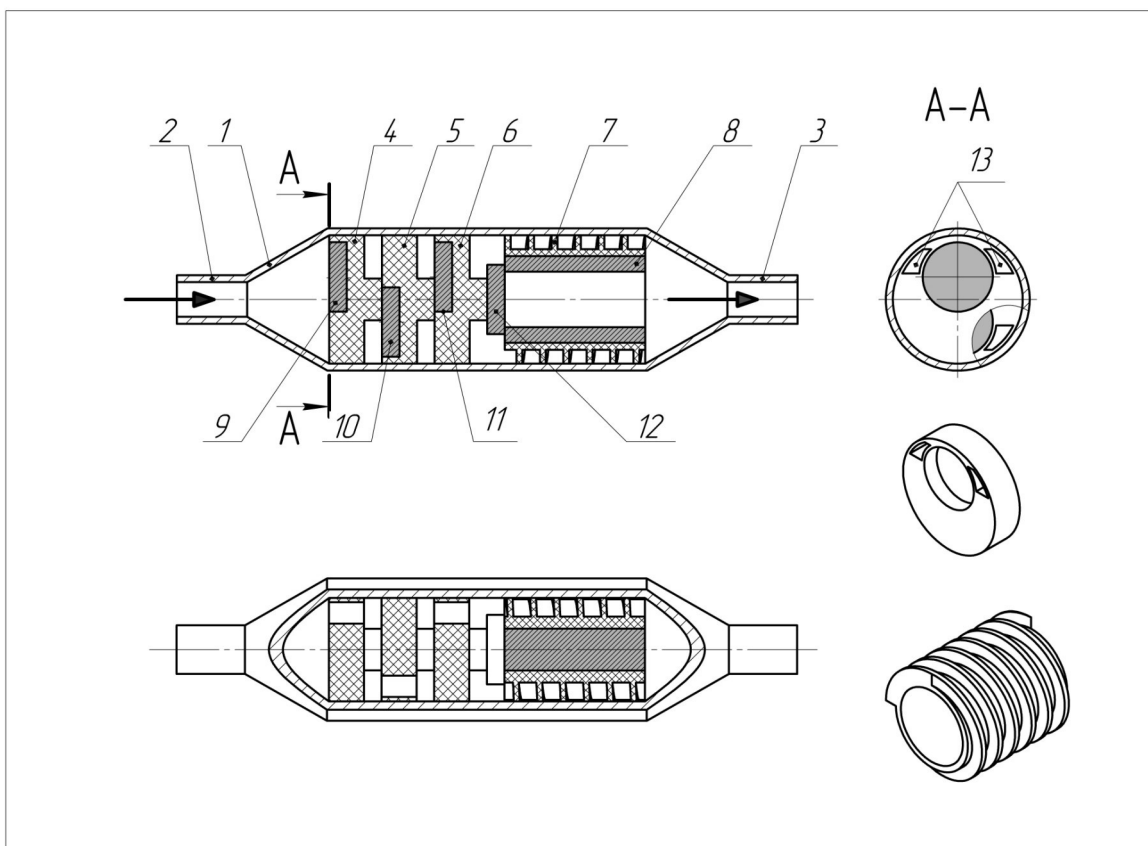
Загальний вигляд пристрою для магнітної обробки палива.
